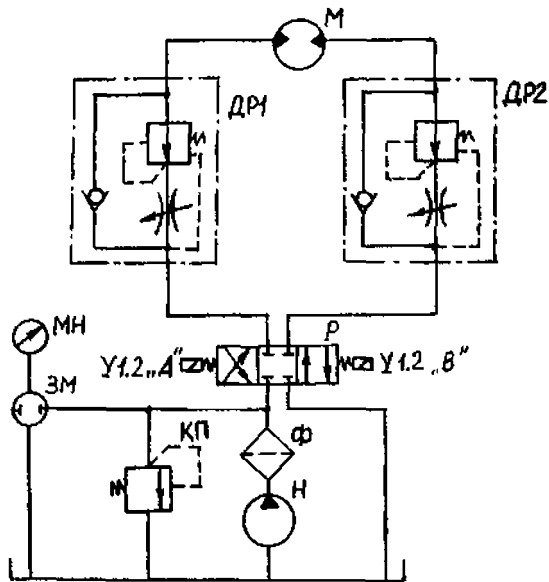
Гидропривод вращения шпинделя токарного станка
